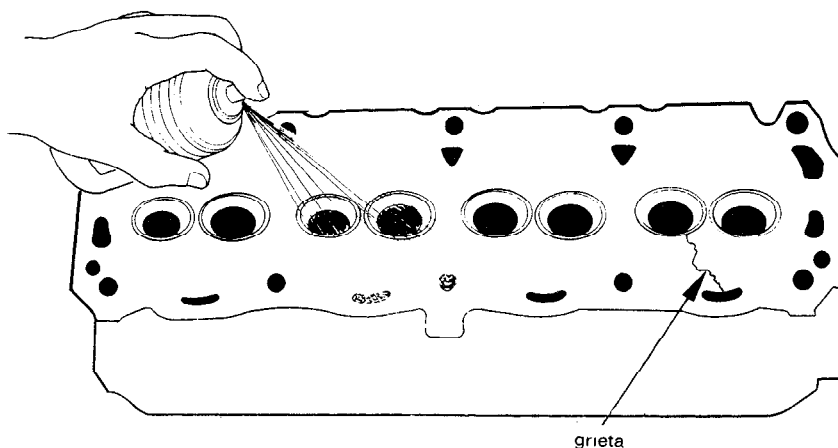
Detección de grietas con tinte penetrante. Se está aplicando el revelador y ha aparecido la grieta en el lado derecho de la culata.
